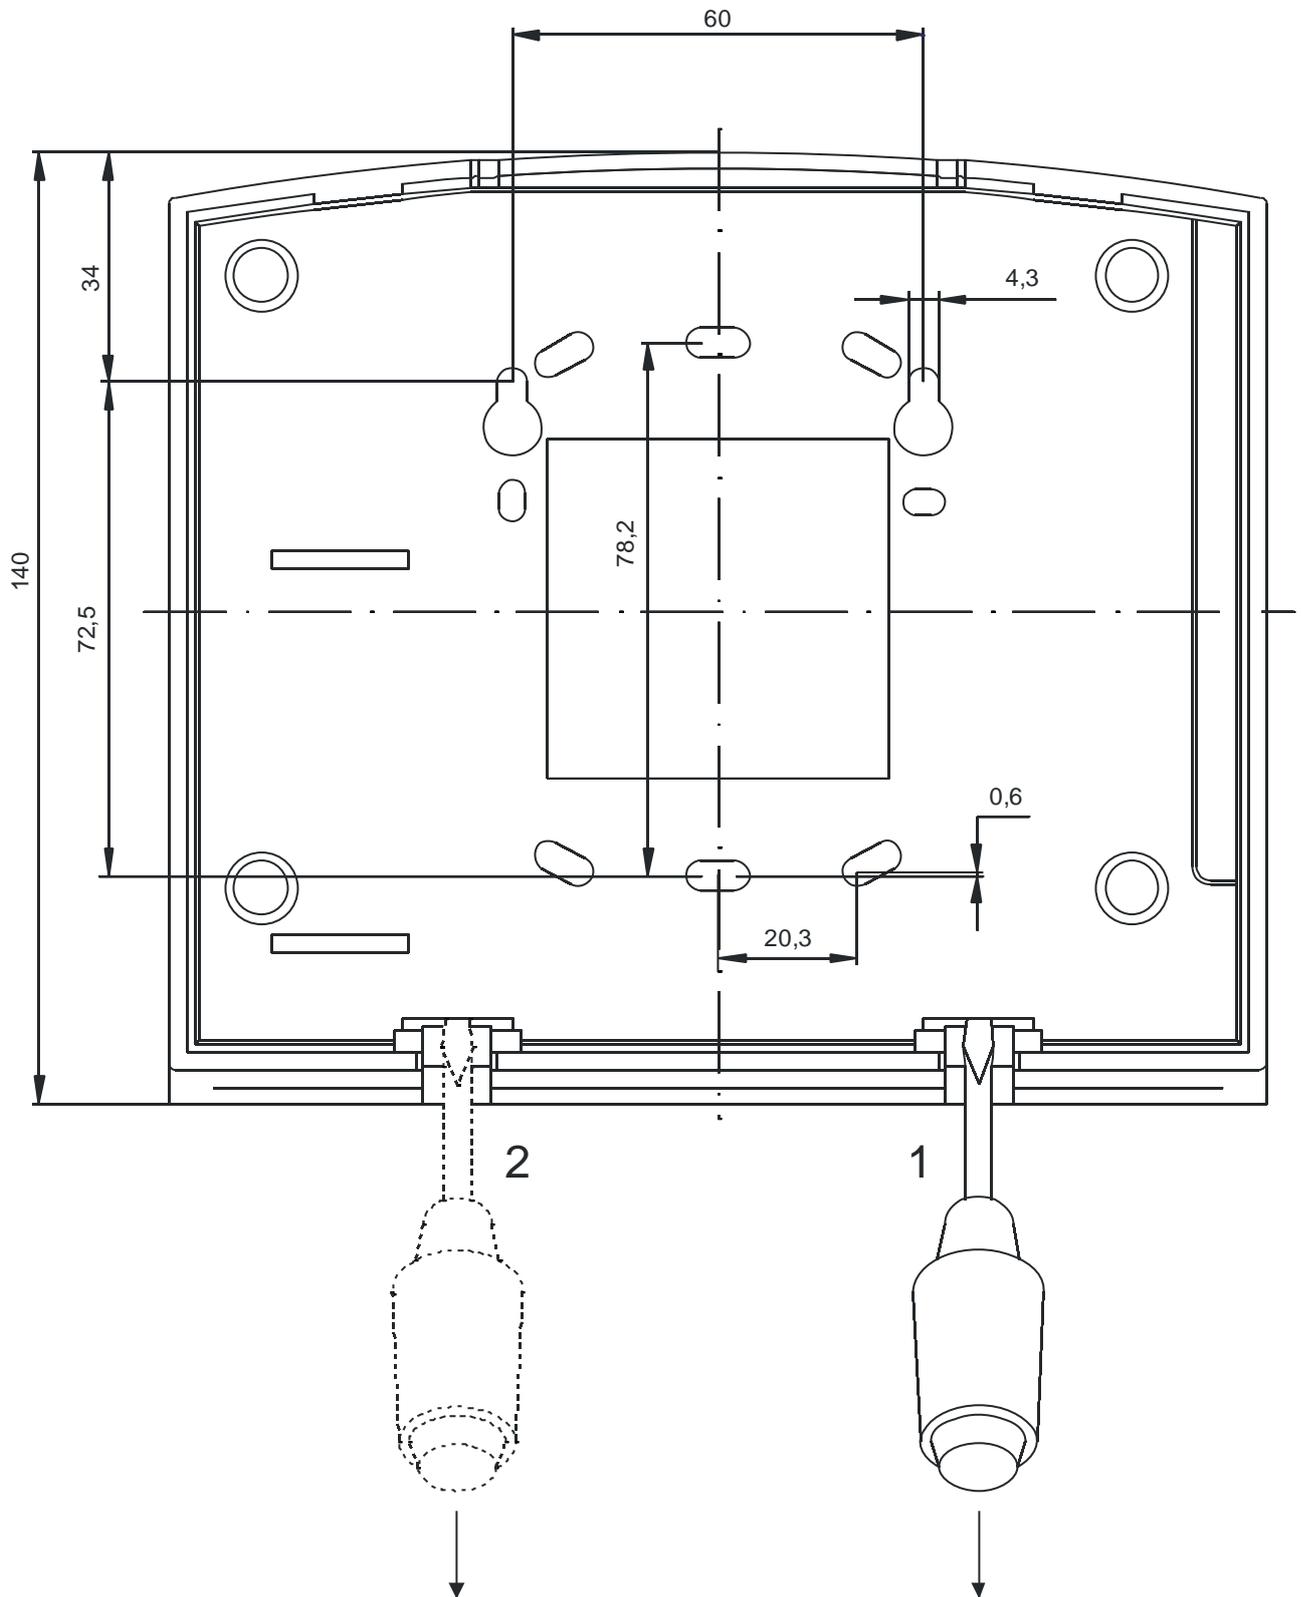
Чертеж отверстий в корпусе для крепления пульта (вид сзади). Порядок разборки корпуса.
